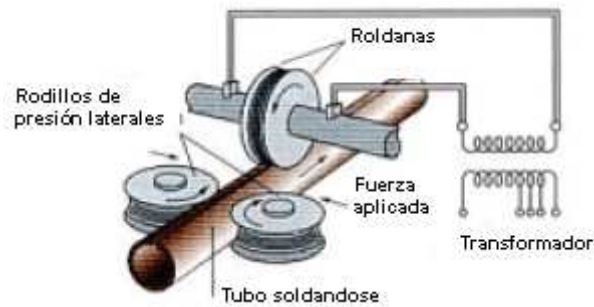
Equipo necesario para la soldadura por costura
